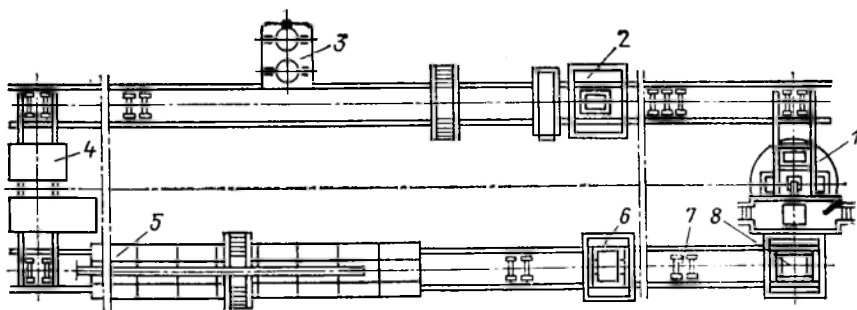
Схема автоматизированной линии изготовления отливок в облицованных кокилях
